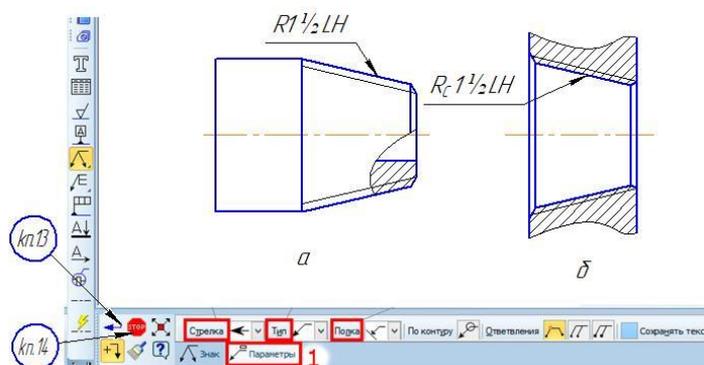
Обозначения наружной и внутренней трубной конической резьбы
